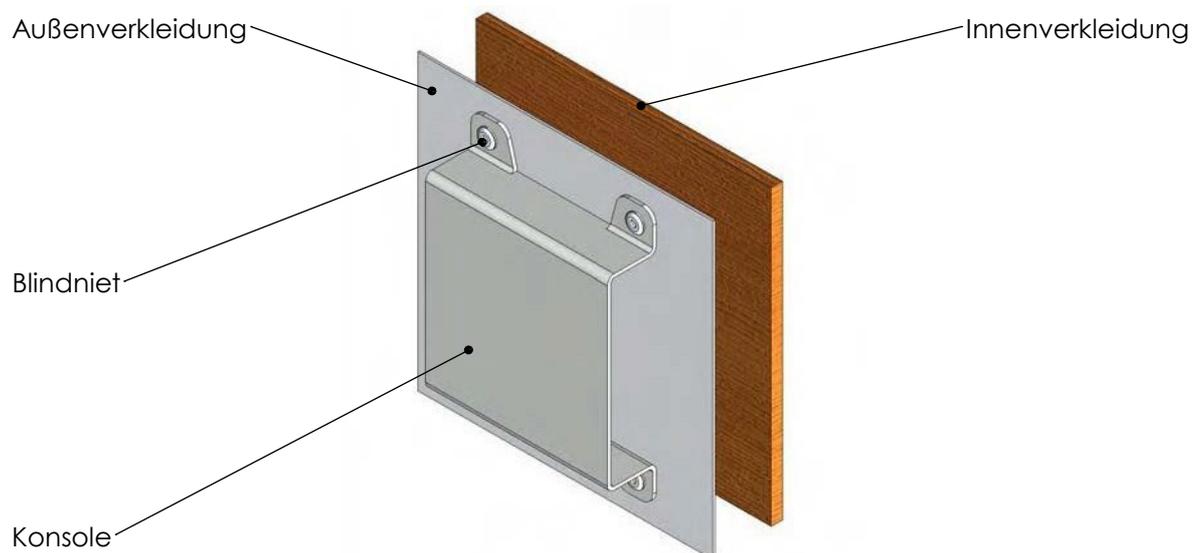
Befestigungsvorschlag für Typenschilder bei Hohlprofilen
